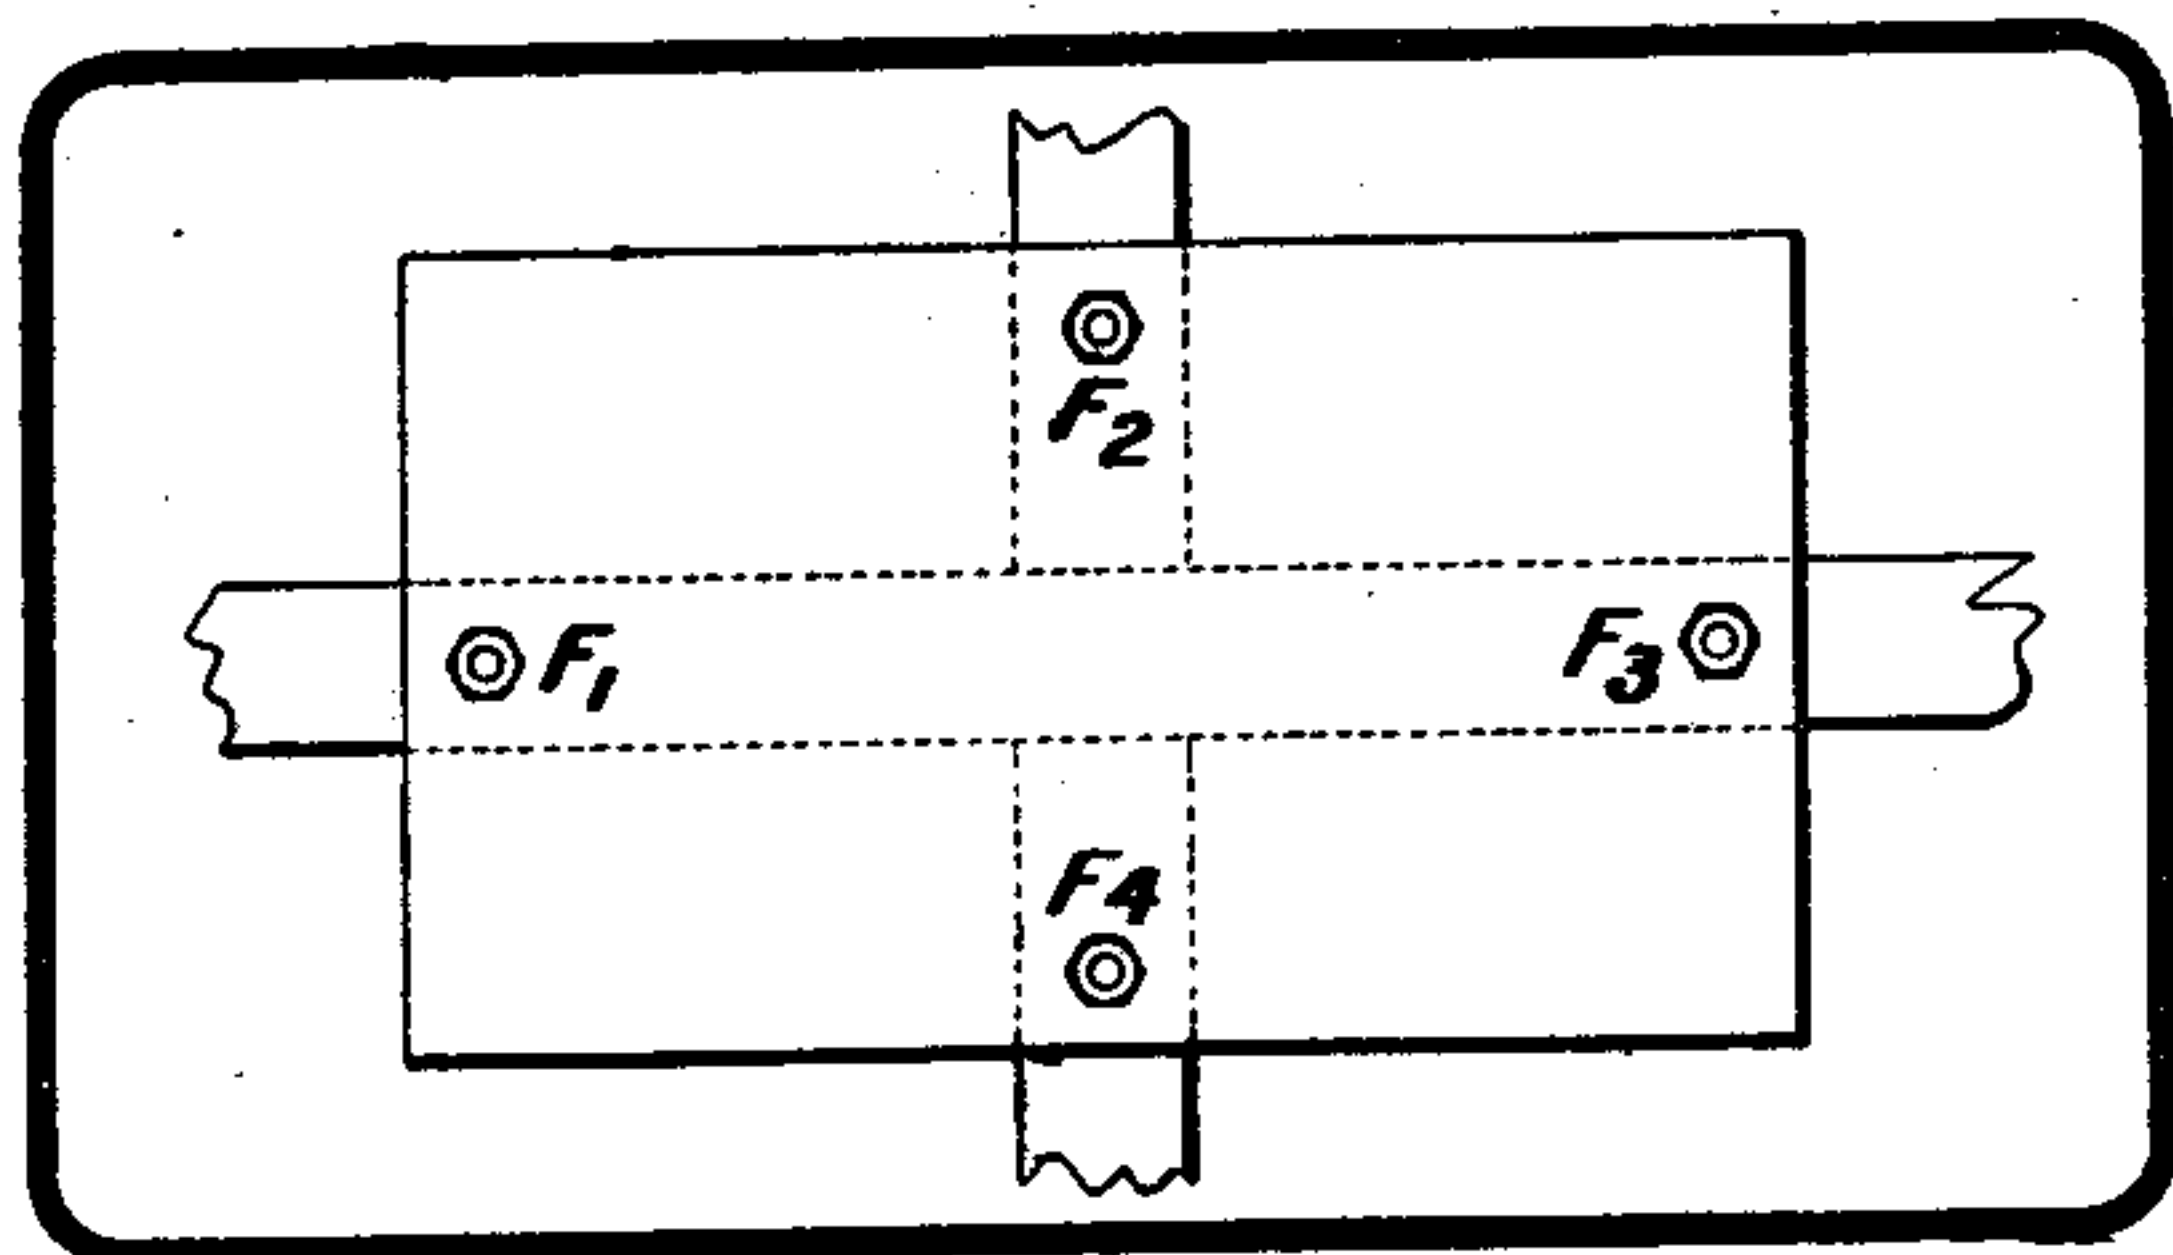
Vue de face de la plaquette supportant les inverseurs et fixée au centre du cadre.
